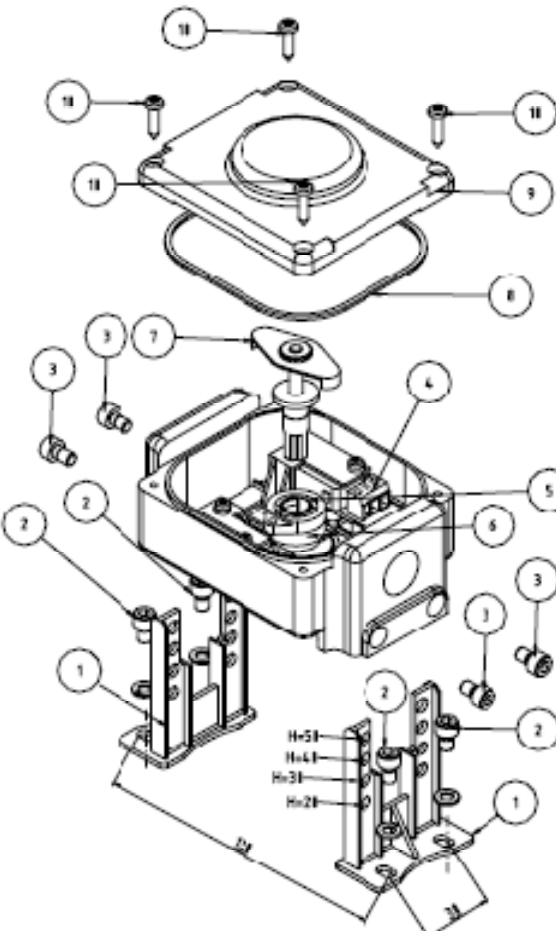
Manual del interruptor posicionador de válvulas de cierre rápido.
